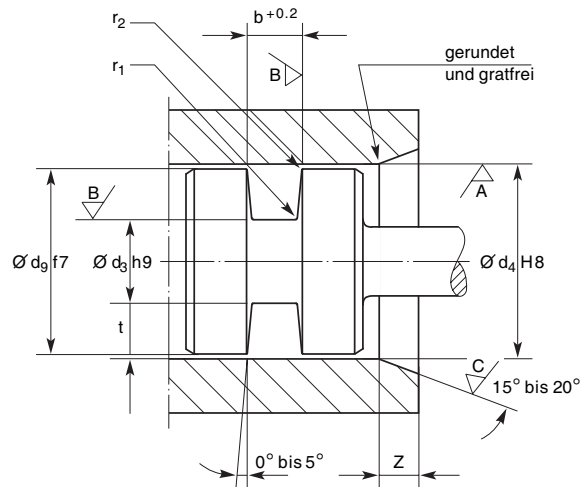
Kolbendichtung – Hydraulik und Pneumatik
